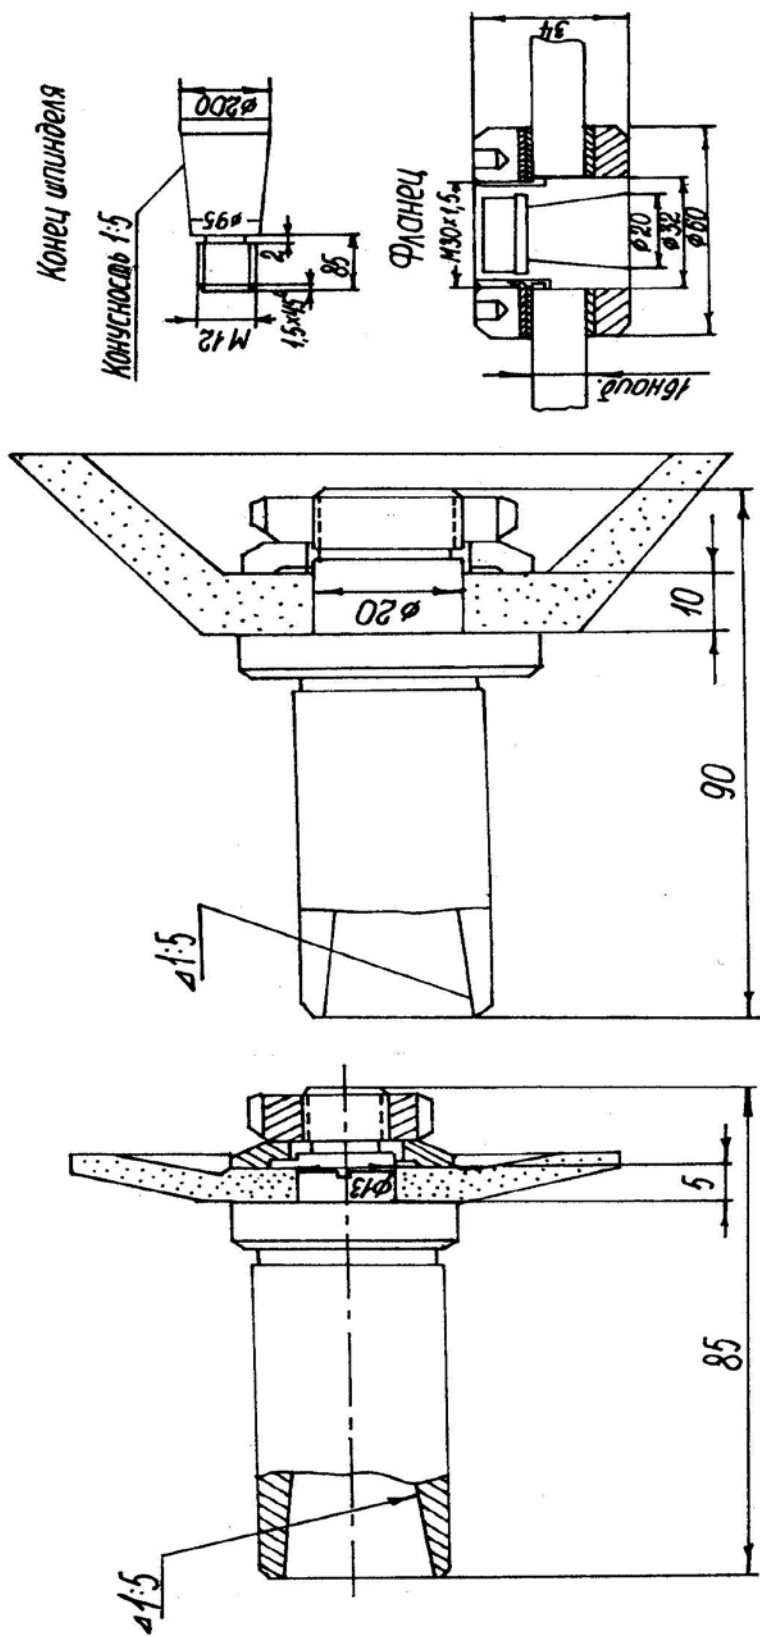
Оправки для закрепления кругов. Основные размеры и посадочные места
